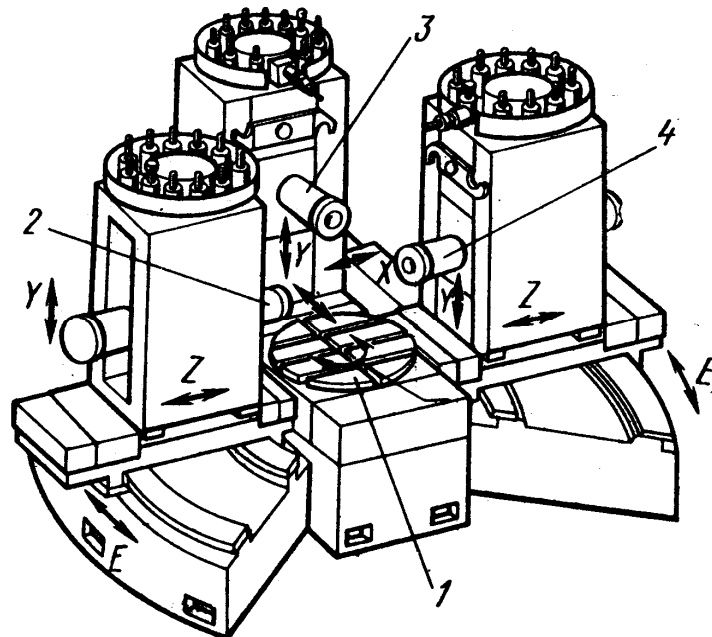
Трестояковий агрегатний верстат з ЧПК АГП 630-400-3.3
